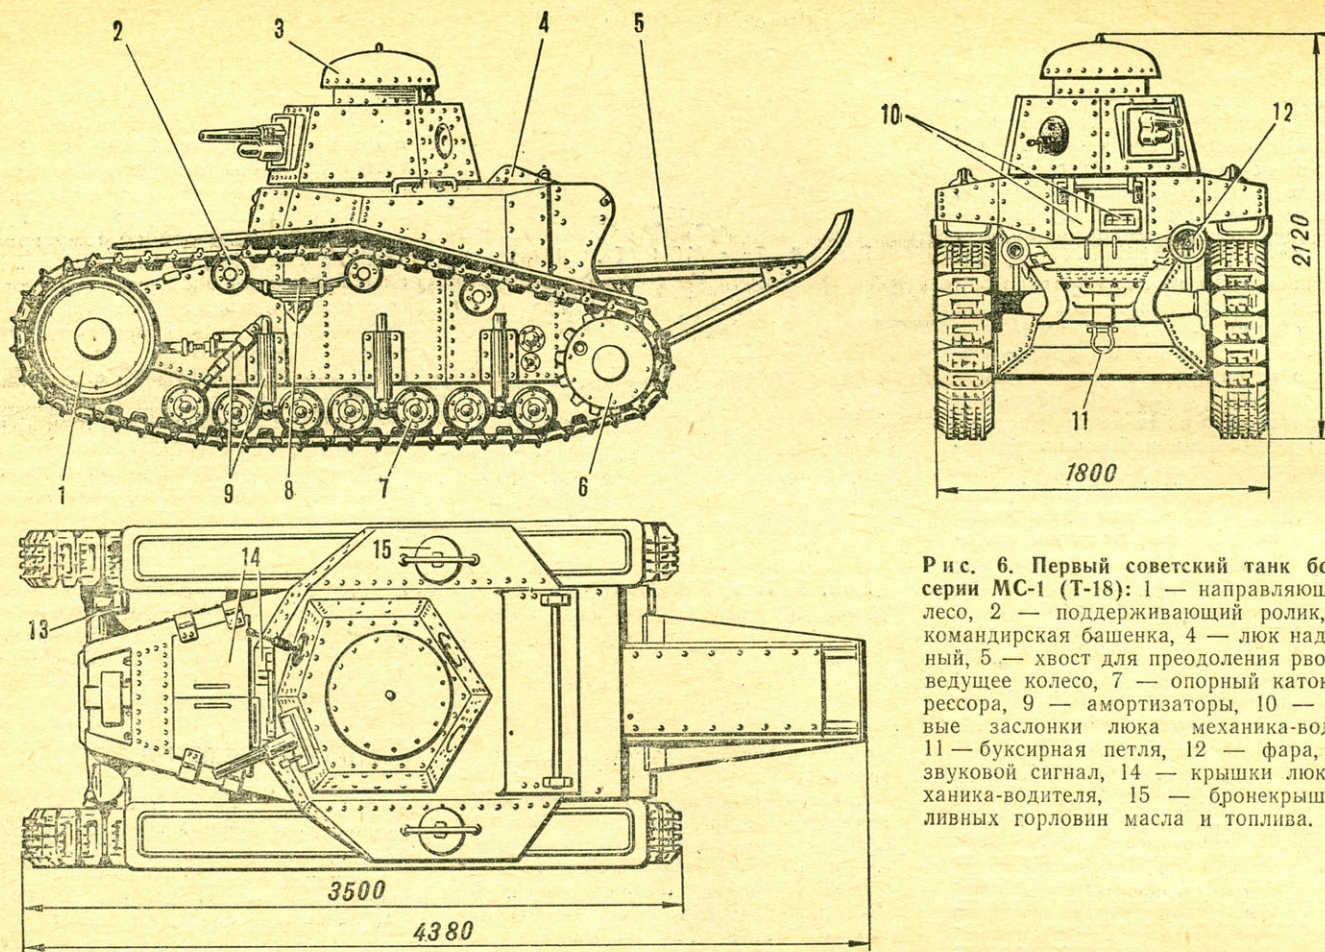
Первый советский танк большой серии МС-1 (Т-18): 1 — направляющее колесо, 2 — поддерживающий ролик, 3 — командирская башенка, 4 — люк надмоторный, 5 — хвост для преодоления рвов, 6 — ведущее колесо, 7 — опорный каток, 8 — рессора, 9 — амортизаторы, 10 — броневые заслонки люка механика-водителя, 11 — буксирная петля, 12 — фара, 13 — звуковой сигнал, 14 — крышки люков механика-водителя, 15 — бронекрышки заливных горловин масла и топлива.
